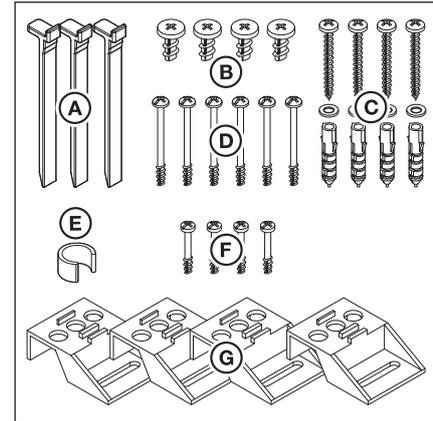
Zubehörbeutel Steuerungsgehäuse
